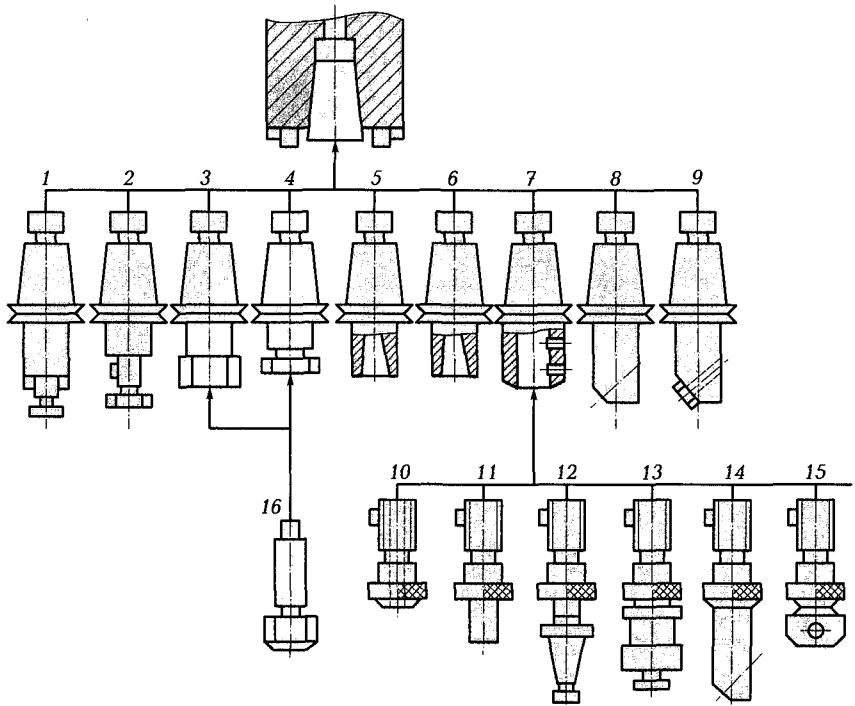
Набор вспомогательного инструмента для станков сверлильно-расточной и фрезерной групп:
